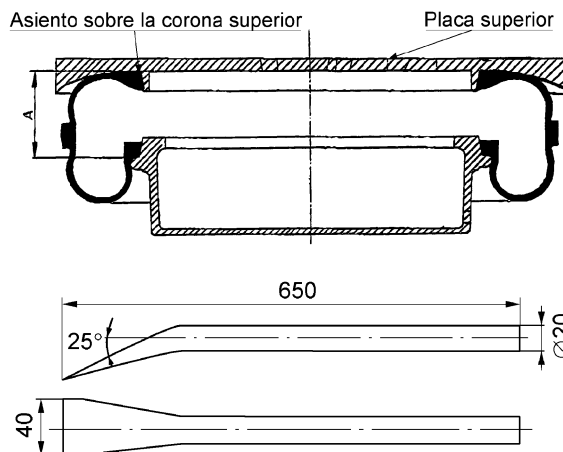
Desmontaje de membrana – Herramienta de desmontaje
